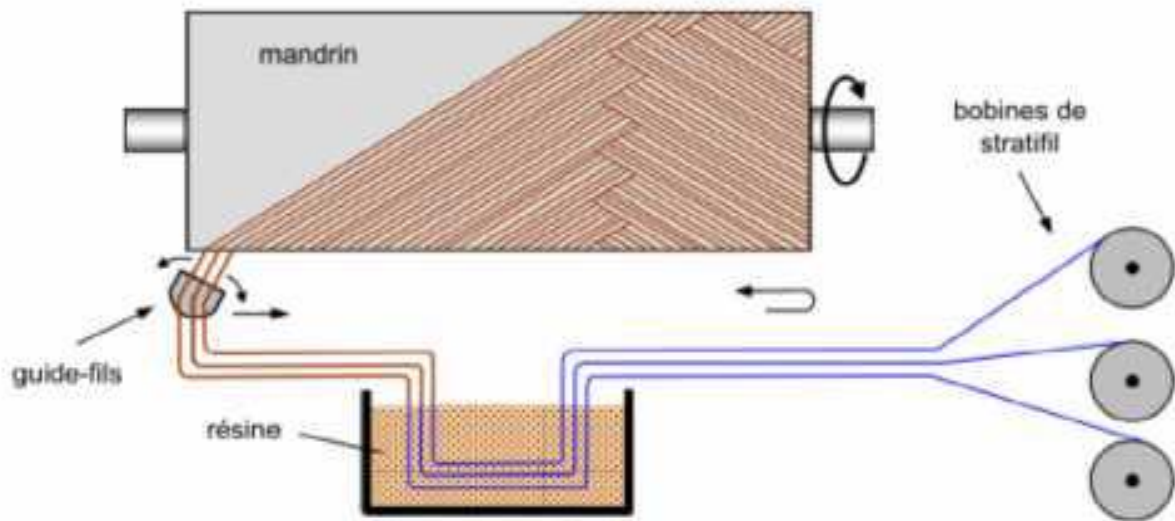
Principe d'enroulement hélicoïdal [2].
